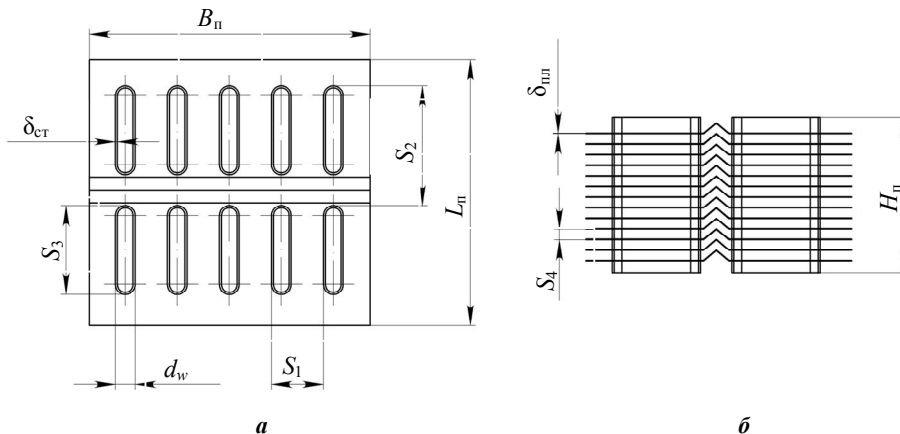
Поверхность теплообмена для ОНВ нового поколения: d_w – высота поперечного сечения трубки; S_1 – расстояние между трубками в поперечном ряду; S_2 – шаг между поперечными рядами трубок; S_3 – наибольший габарит поперечного сечения трубки; S_4 – шаг между ребрами; $\delta_{ст}$, $\delta_{пл}$ – толщины стенки трубки и пластины оребрения соответственно; H_n , L_n и B_n – соответственно высота, длина и ширина пучка
